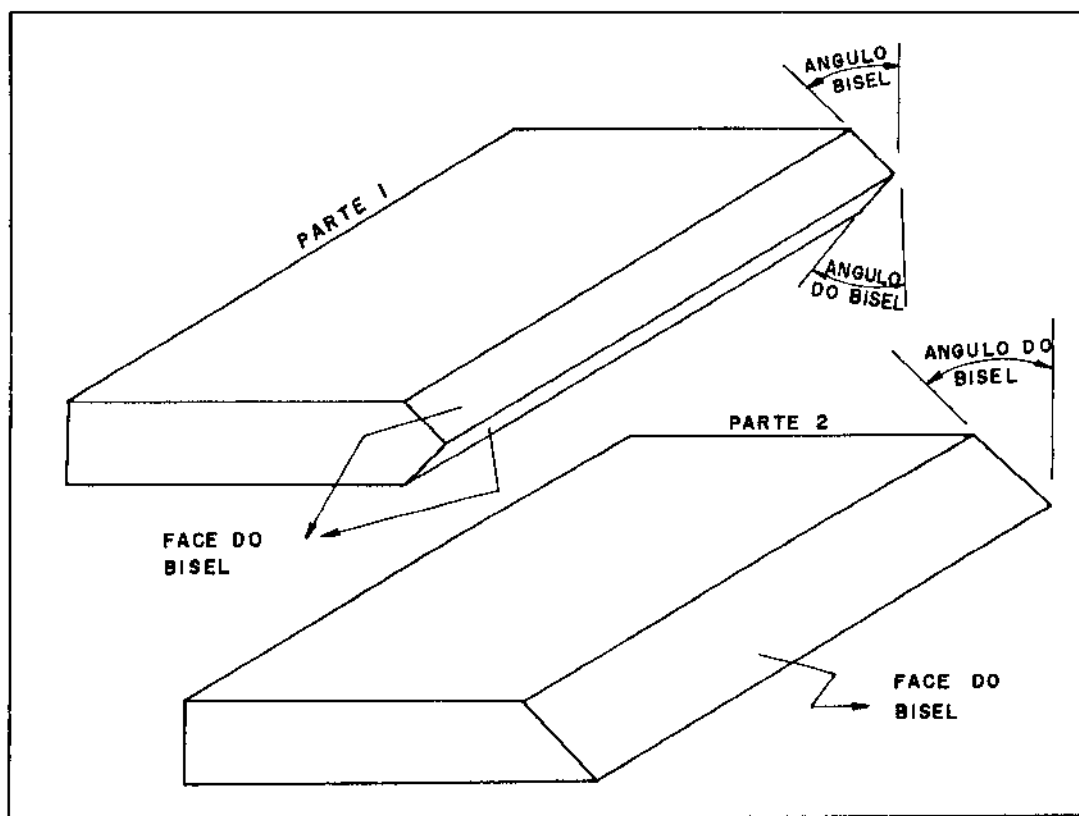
Desenho do Corpo-de-Prova Tekken Destacando as Partes 1 e 2.
